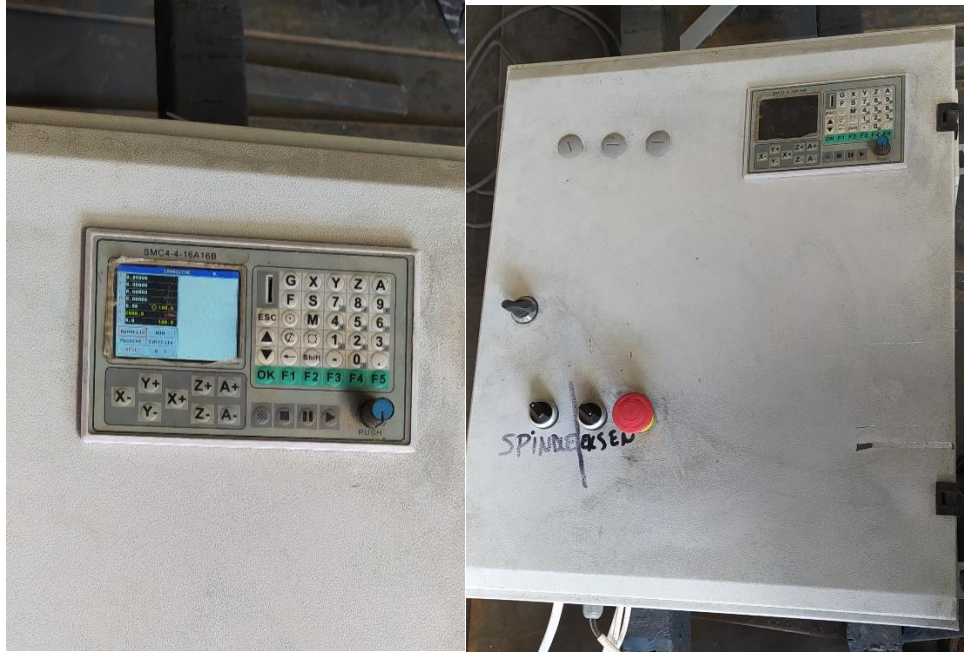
CNC Router Mekanik Kısım Son Montajı-4
